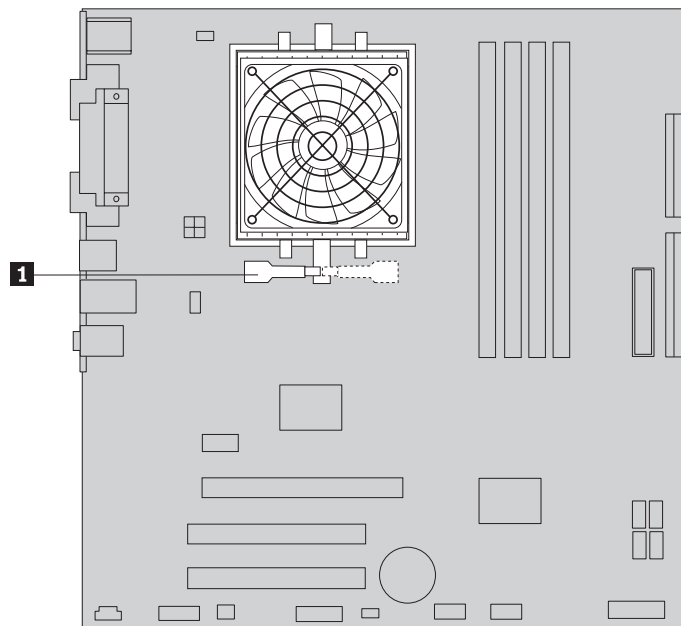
Odstránenie chladiča pripevneného skrutkami
